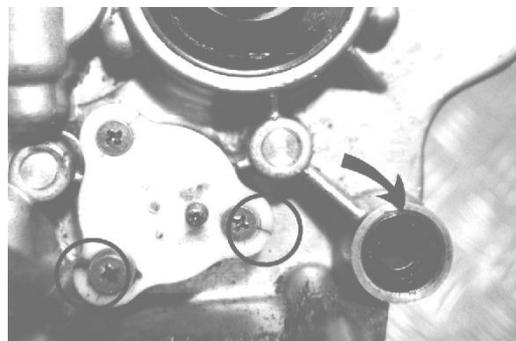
Eingerissene Abdeckung am Leerlaufschalter und O-Ring Schaltwelle
